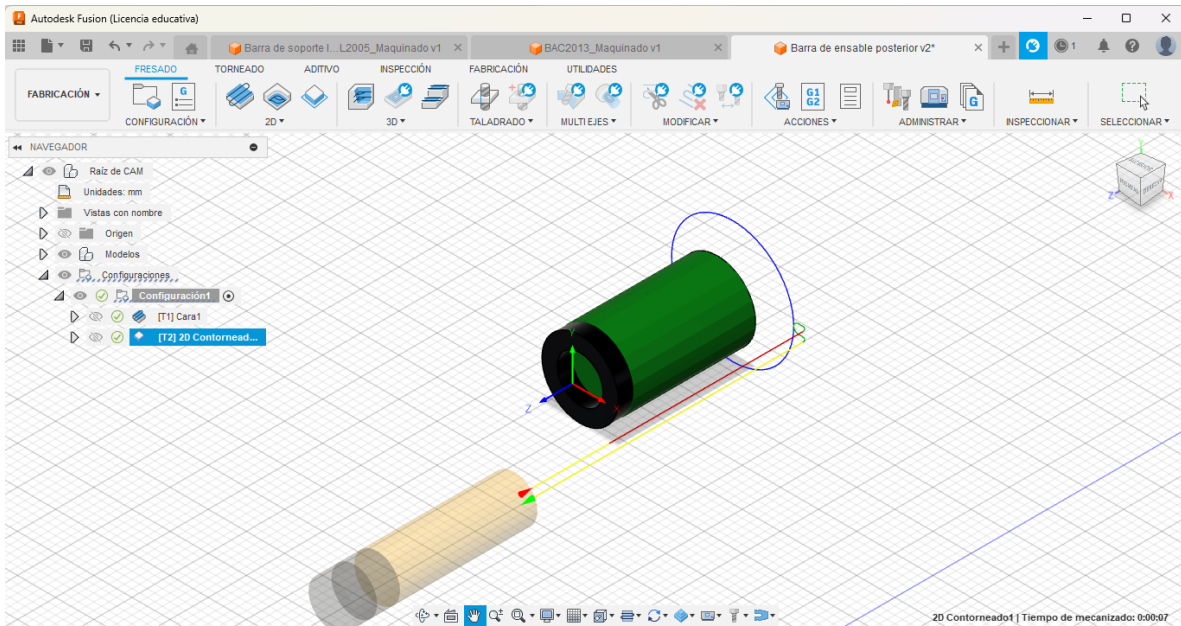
Maquinado de la pieza Barra de ensamble posterior BAE2015
